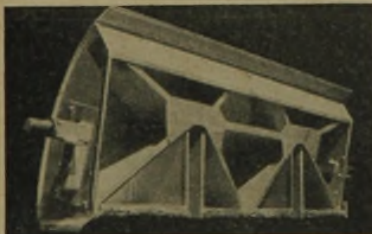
Preßkolben einer Strohpresse in Stahlblechkonstruktion
